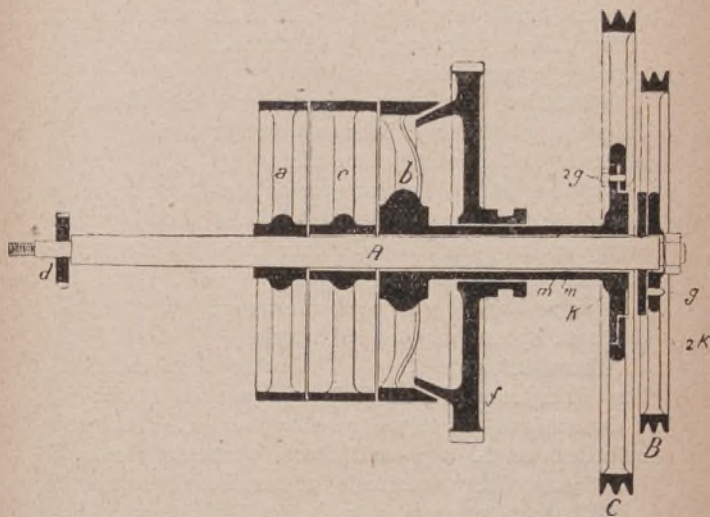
[49]. — Dettagli dell'albero motore *A*, puleggie di marcia e torsione.
